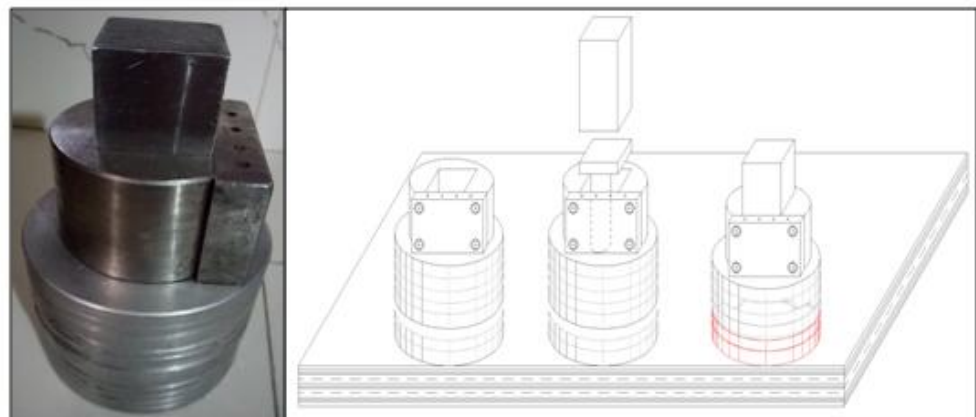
20 Image du moule en acier fabriqué en laboratoire pour le moulage des pastilles.
